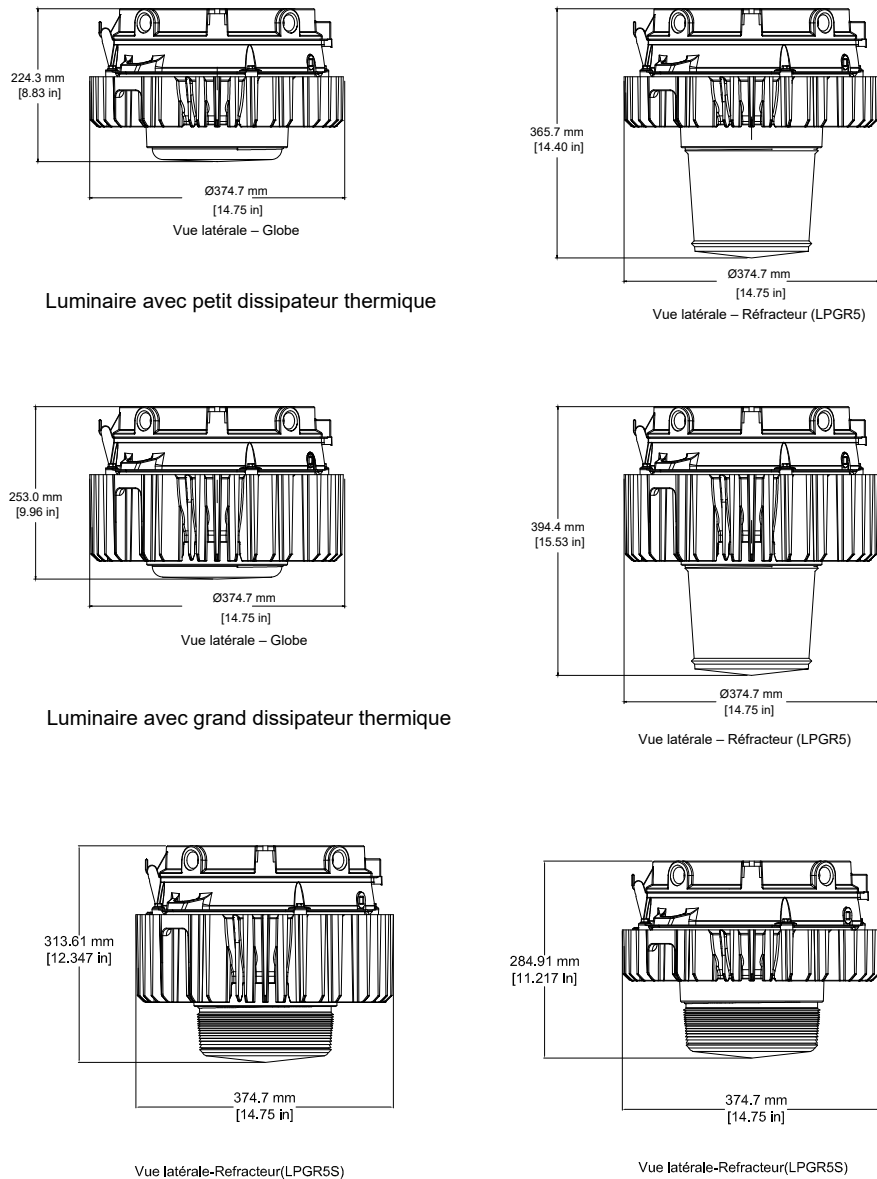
LUMINAIRE AVEC CAPOT DE PLAFOND
